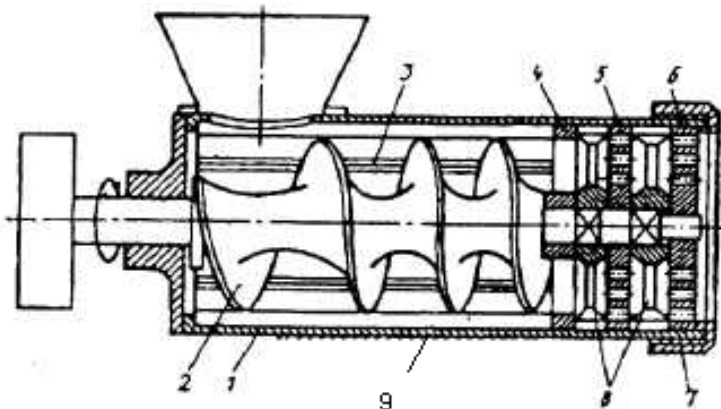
Принципова схема вовчка: 1 – робоча камера; 2 – шнек; 3 – ребра; 4 – підрізні решітки; 5,6 – ножові решітки; 7 – затискна гайка; 8 – ножи; 9 – корпус
